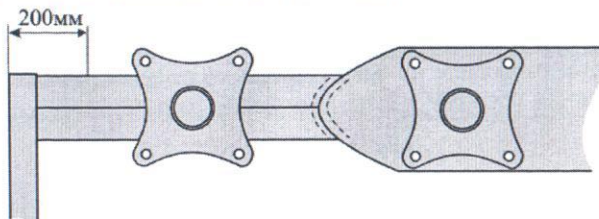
Контроль околошовной зоны сварного соединения накладок с нижним поясом продольных балок рамы
